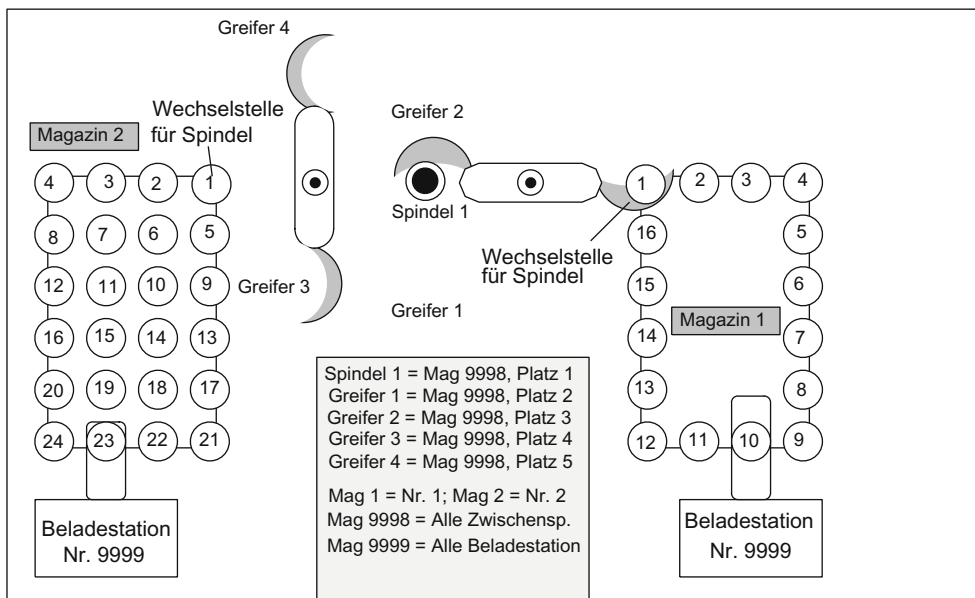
Werkzeugmaschine mit Ketten- und Flächenmagazin
